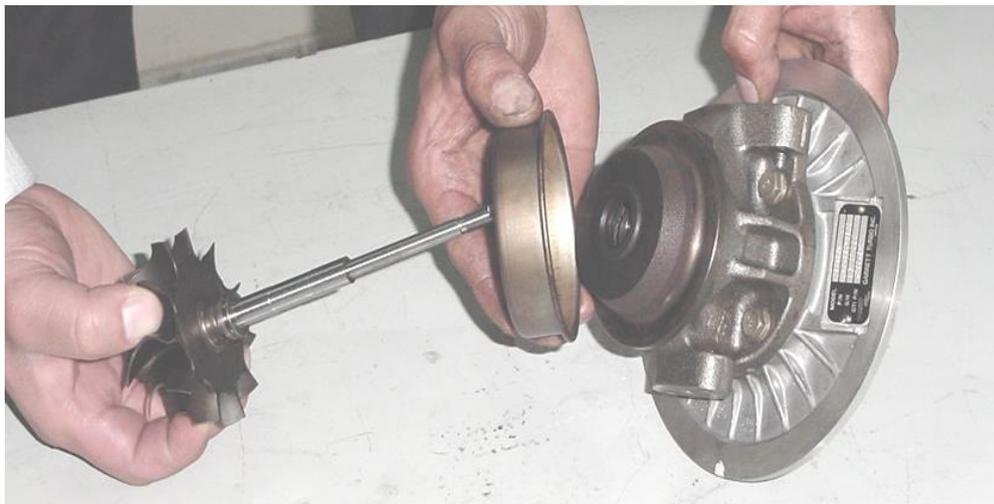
Turbina de escape (izquierda) y eje común o flecha (centro) (General Motors, 2012),
